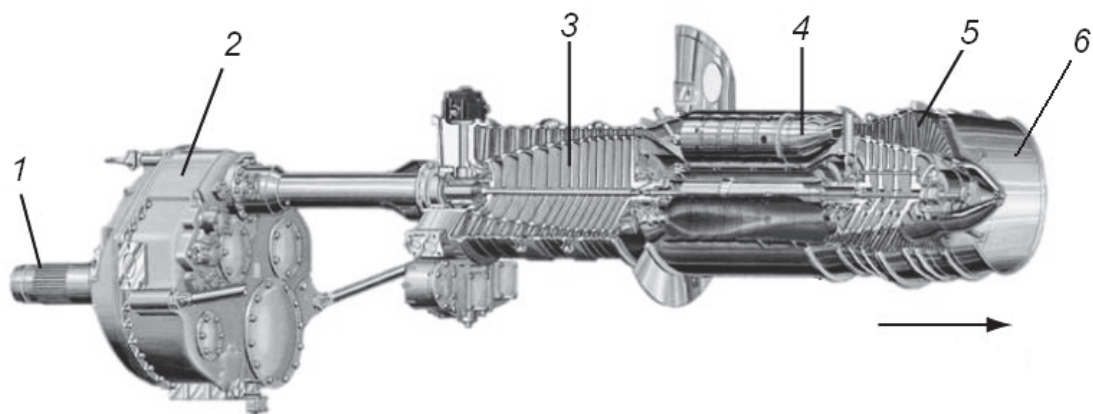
Конструктивная схема турбовинтового двигателя:
